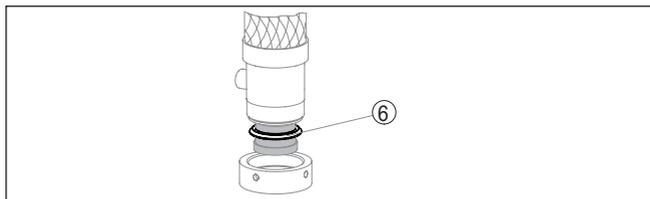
Kit de montage - flexible réfrigérant du scintillateur - bas
